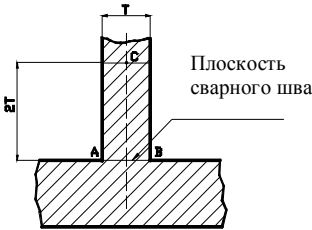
Положение точки срединной плоскости, напряжение в которой равно номинальному для сварного соединения
